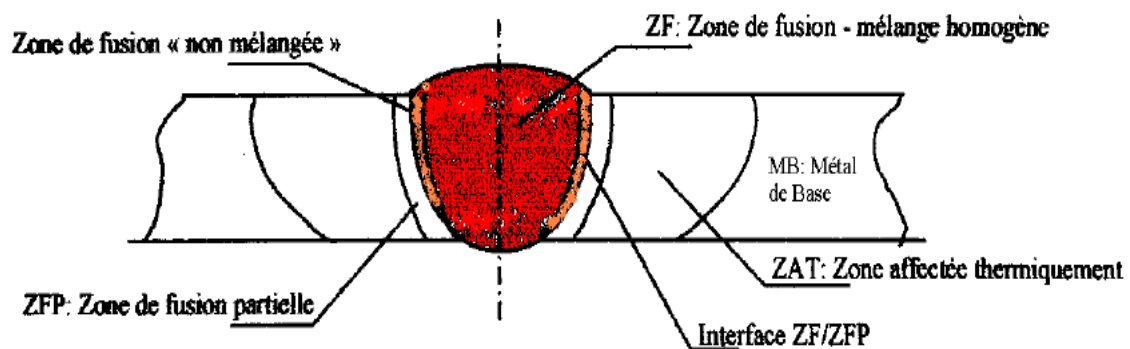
Soudure autogène bout à bout sur chanfrein en V[2].
